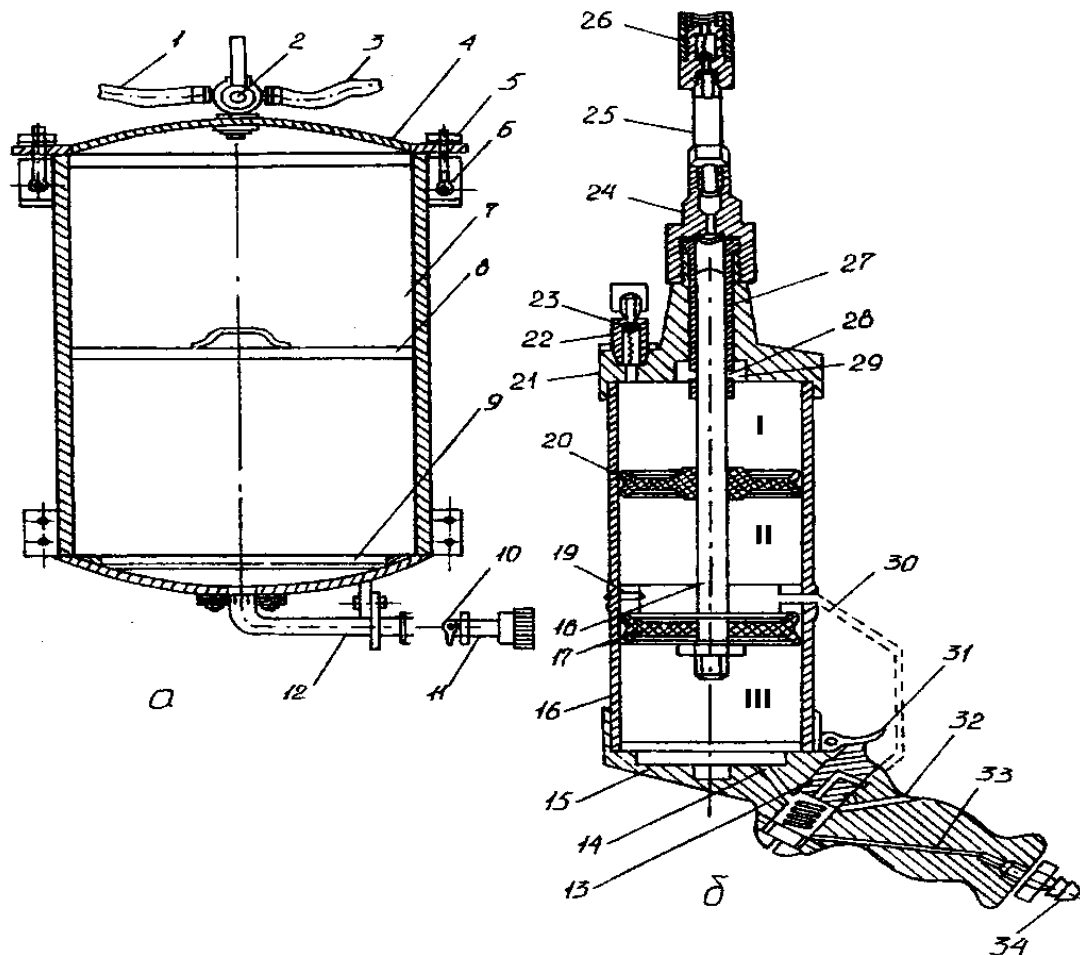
Пневматический смазочный нагнетатель ОЗ-1153А:
